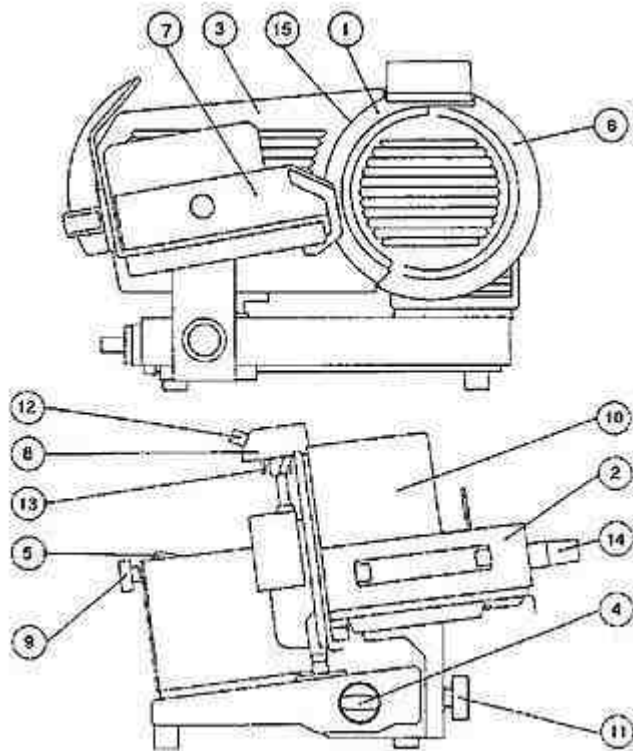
Будова слайсера: 1 – ніж (лезо); 2 – каретка; 3 – калібрована пластина; 4 – регулятор товщини скибочки; 5 – перемикач; 6 – захист ножа; 7 – штовхач продукту; 8 – точило ножа; 9 – ручка блокування захисту ножа; 10 – запобіжник для пальців; 11 – ручка блокування каретки; 12 – кнопка точила; 13 – пристосування для зняття заусенців; 14 – ручка штовхача продуктів; 15 – ріжуча крайка
